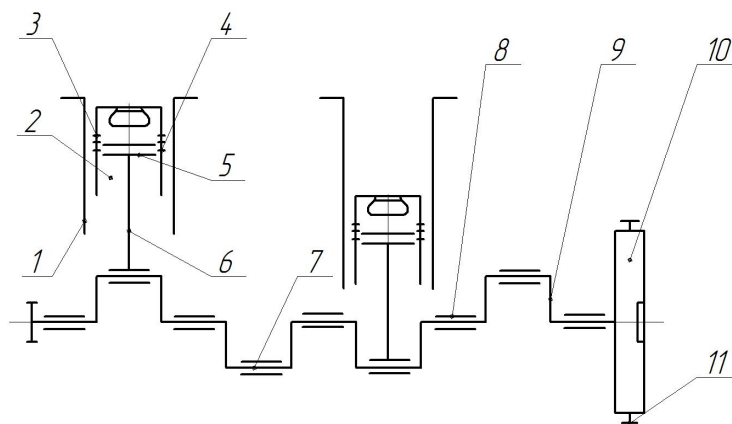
Схема кривошипно-шатунного механизма двигателя Д-243:
